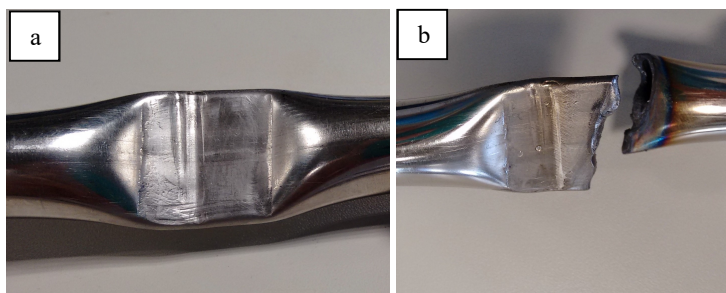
Corte e soldagem. a) Antes. b) Depois.
